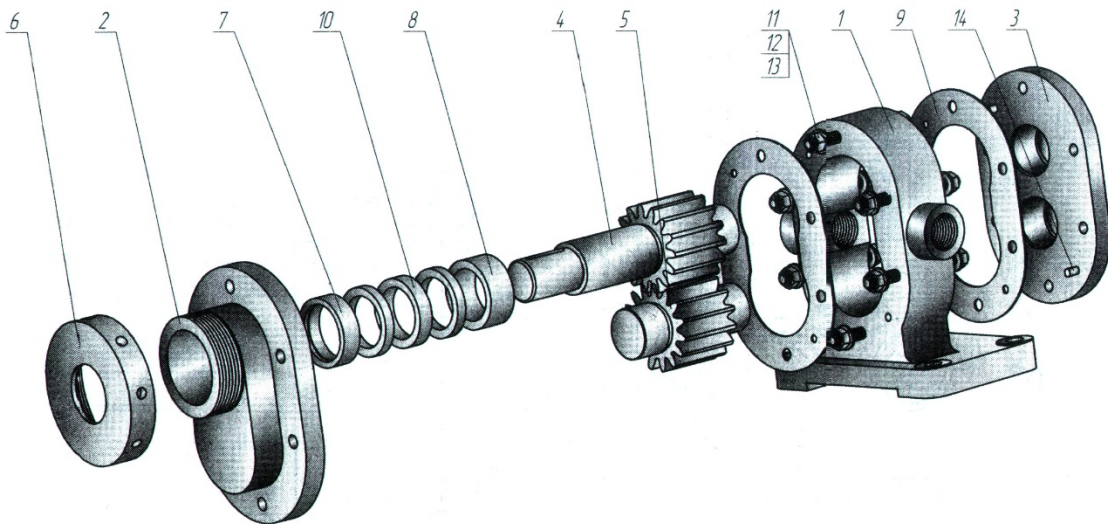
Подетальное расчленение узла: 1 – корпус; 2 – крышка сквозная; 3 – крышка; 4 – вал-шестерня; 5 – колесо ведомое; 6 – гайка круглая; 7, 8 – втулки; 9 – прокладка; 10 – кольцо; 11 – гайка; 12 – шайба; 13 – шпилька; 14 – штифт.
